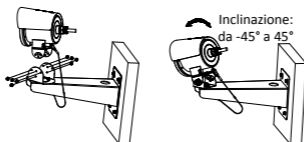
Fissare la telecamera alla staffa di montaggio a parete
